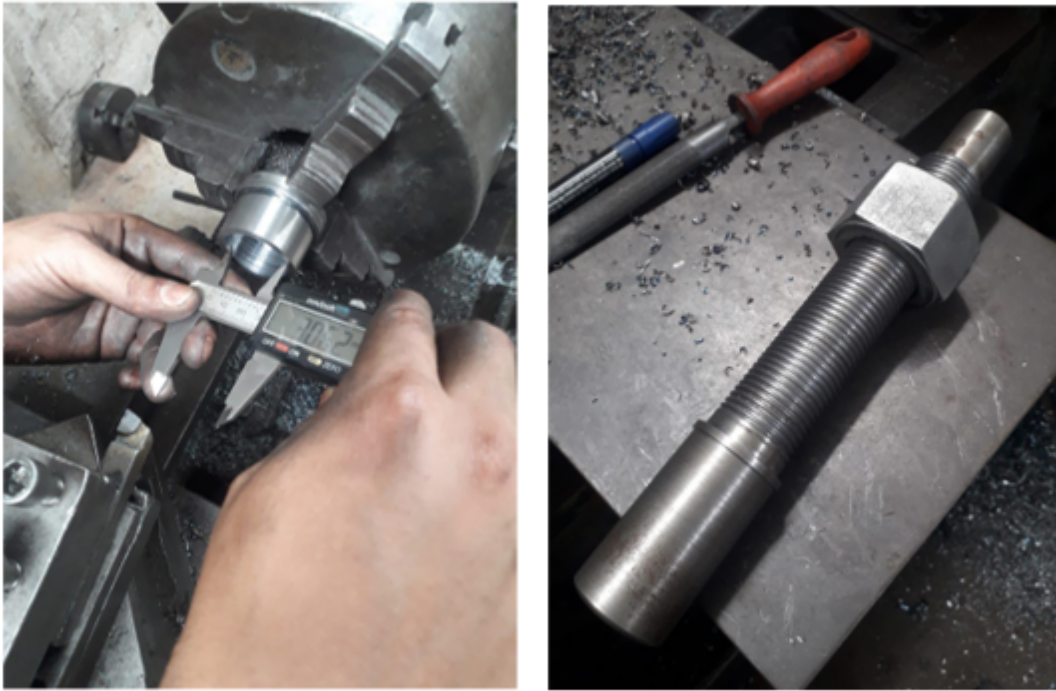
Toma de medidas para mecanizar con tolerancias dimensionales. Elaborado por autores.
